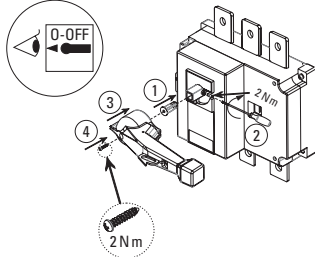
а – Монтаж ручки на корпус рубильников 160-630 А
